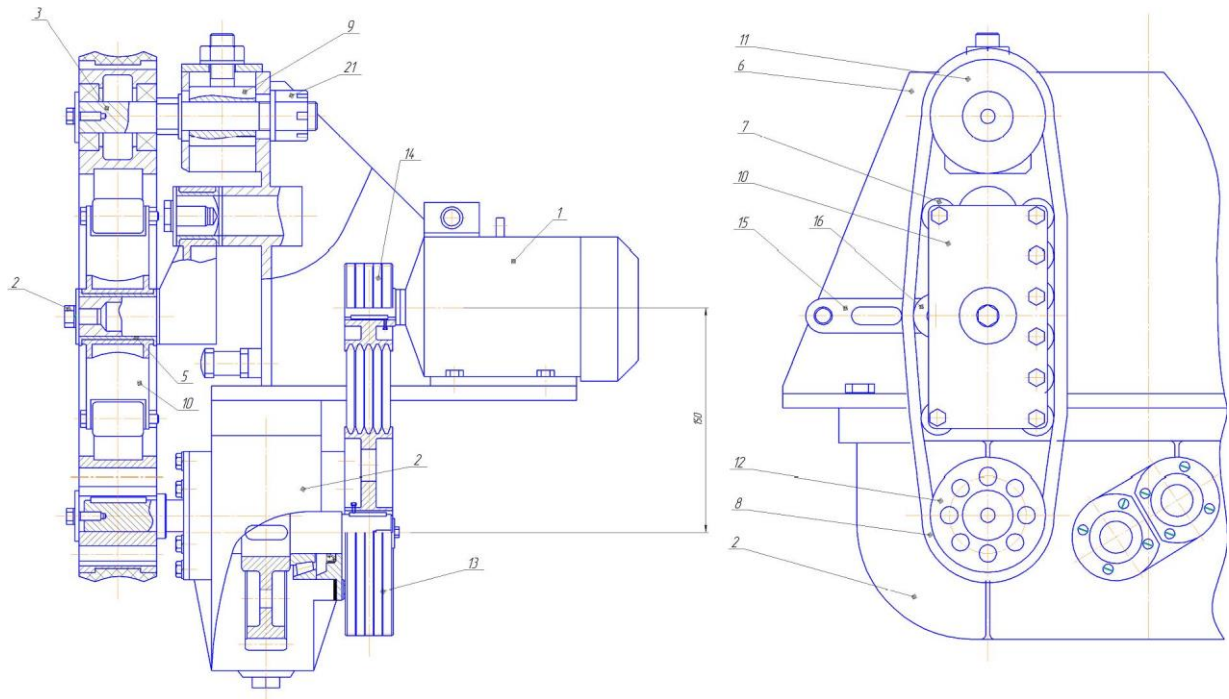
Пристрій протягування плівки: 1 – двигун; 2 – редуктор;
